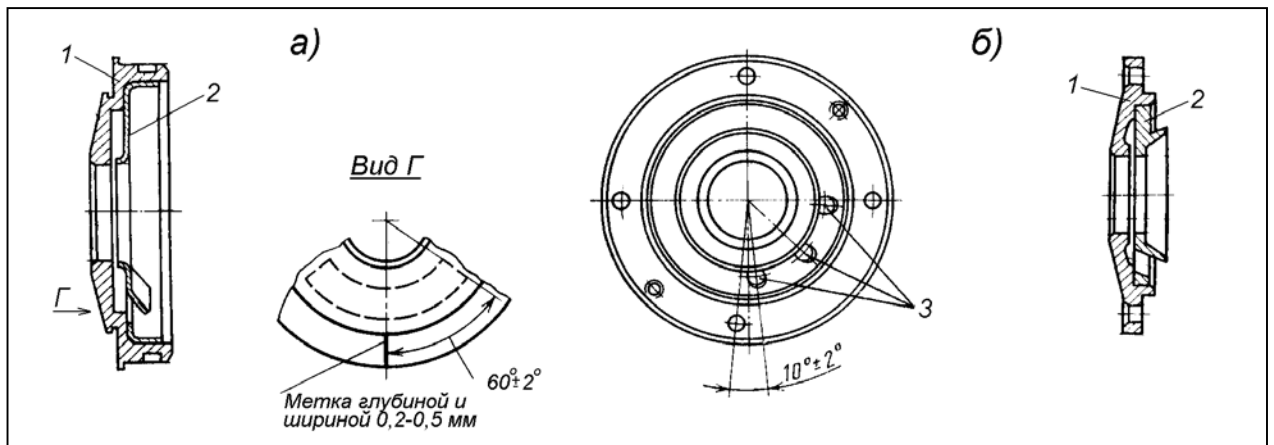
К сборке диска уплотнения компрессора с щитком:
